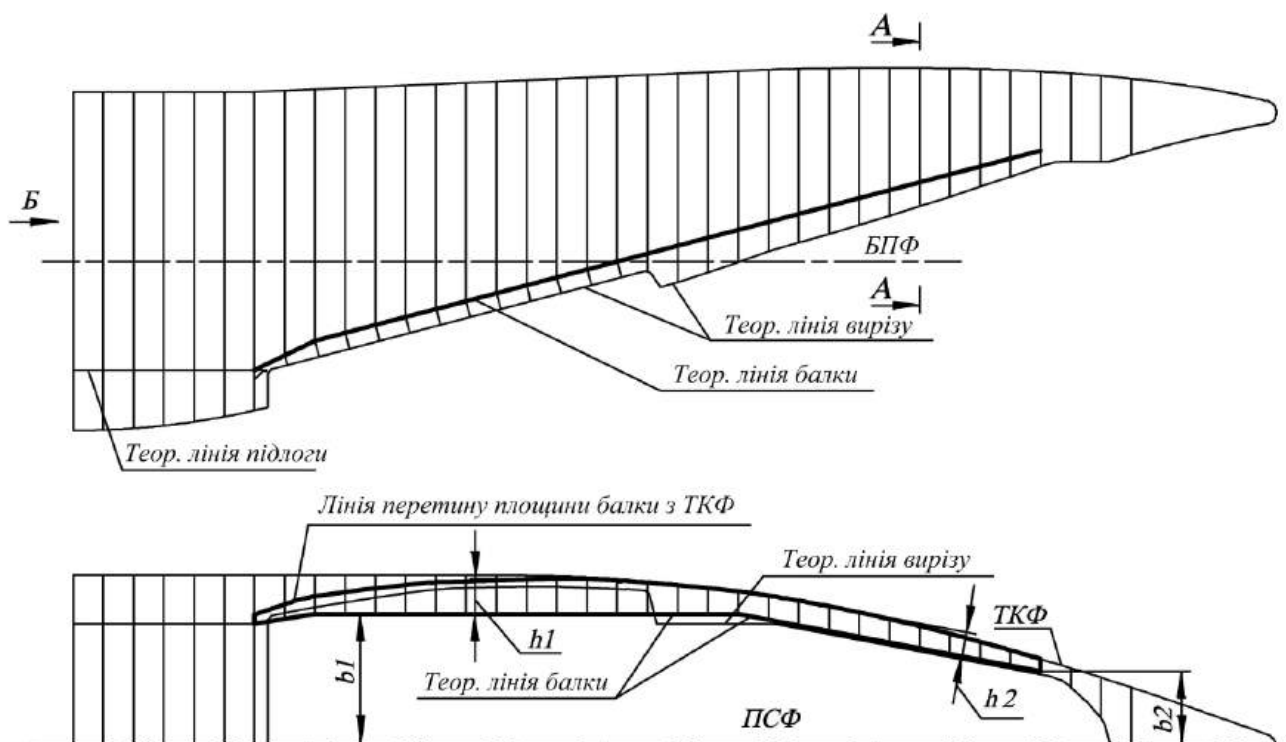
Схема побудови плоскої балки вантажного люка
